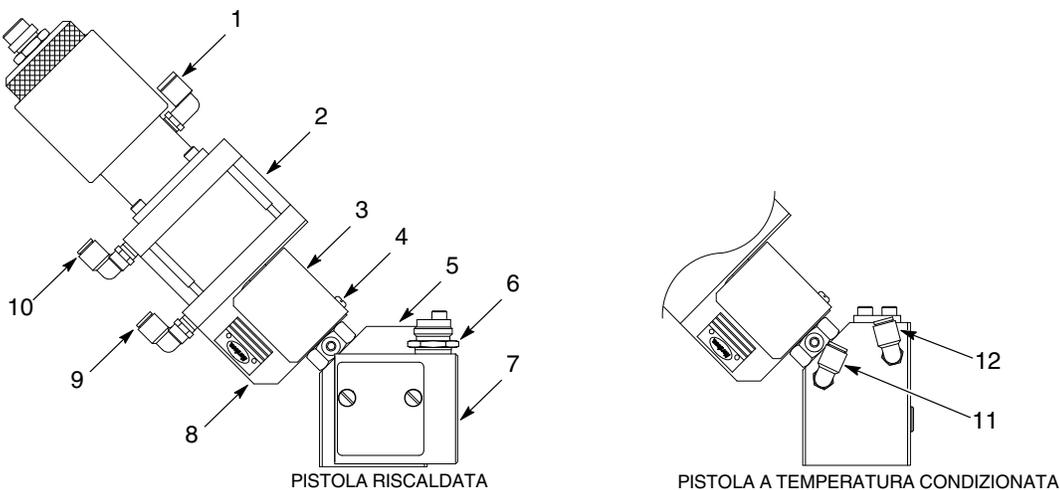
Smontaggio della pistola CE20 dal dispositivo di montaggio (tipico)
